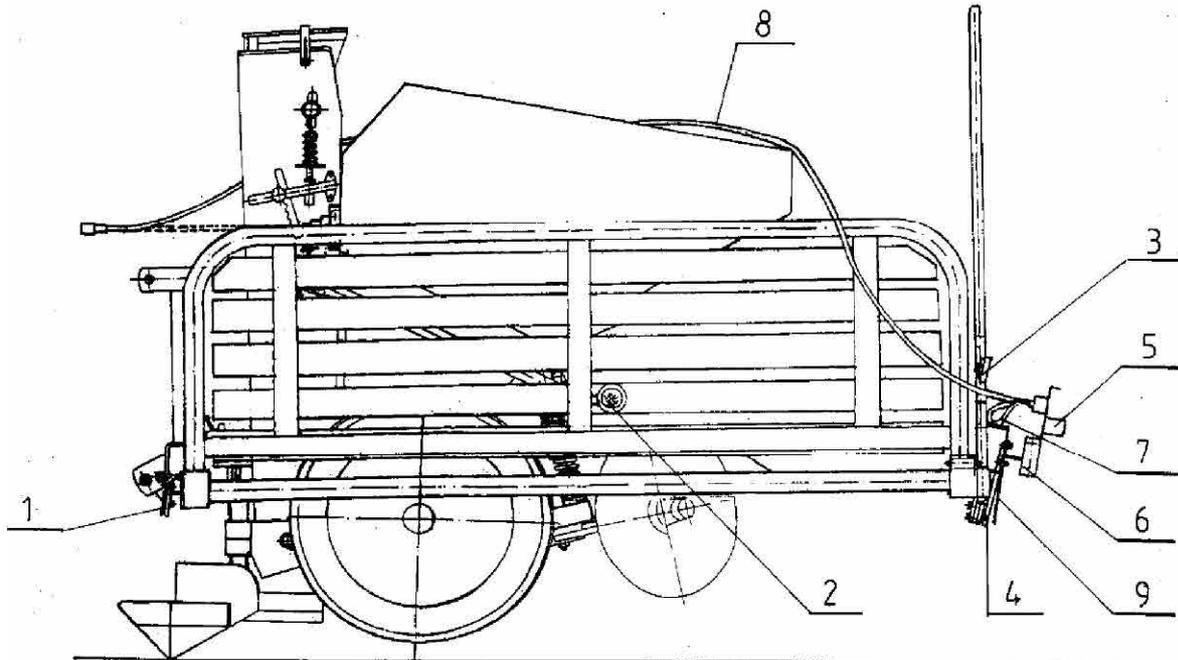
Montageschema der Beleuchtungsanlage auf der Legemaschine.
